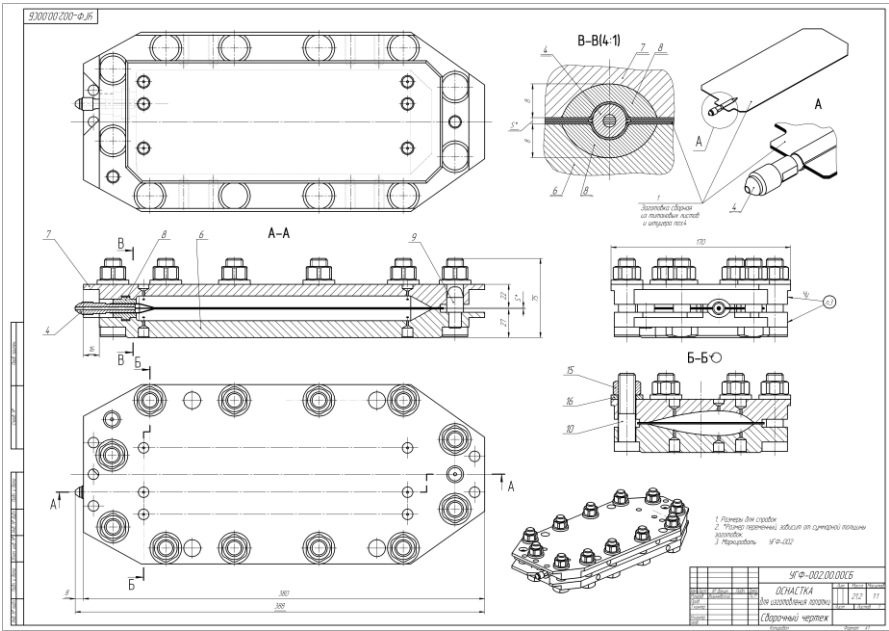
Пристрій УГФ-002.00.000 для дослідження деформування елементів порожнистої лопатки: 1 – заготовка збірна з штуцером 4; 6 – матриця нижня; 7 – матриця верхня; 8 – напіввтулка (в залежності від товщини заготовки має різне виготовлення); 9 – дві колонки направляючі; 10 – болт; 15 – гайка; 16 – шайба
